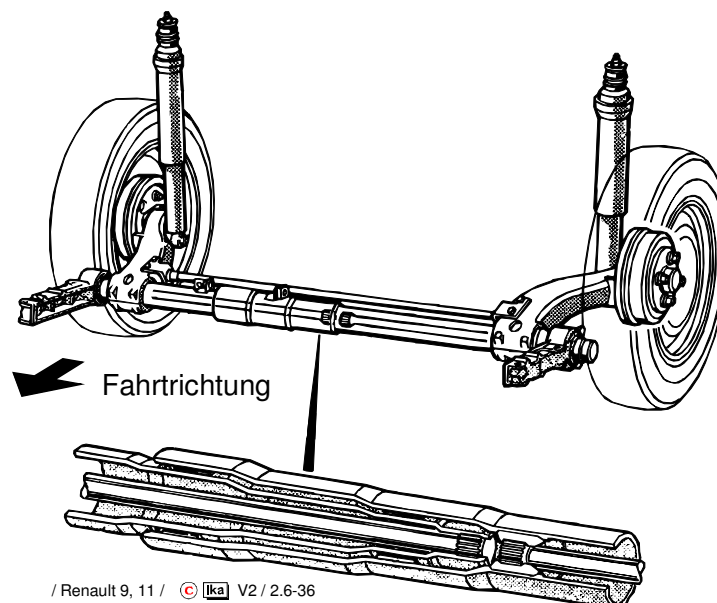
Längslenker - Hinterradaufhängung mit Drehstabfederung (Renault 9, 11)
